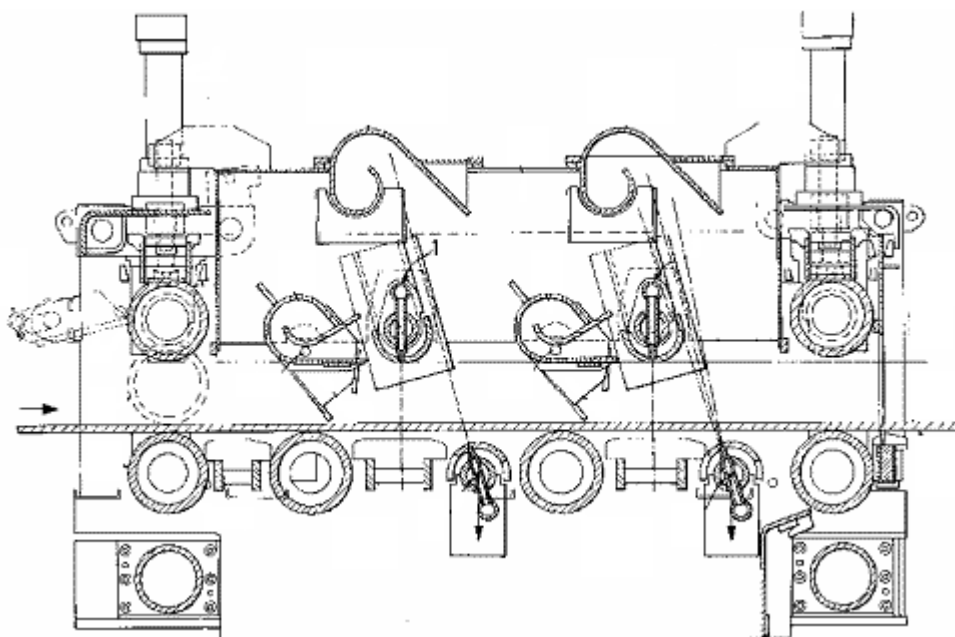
Агрегат для удаления окалины с непрерывнолитой полосы
